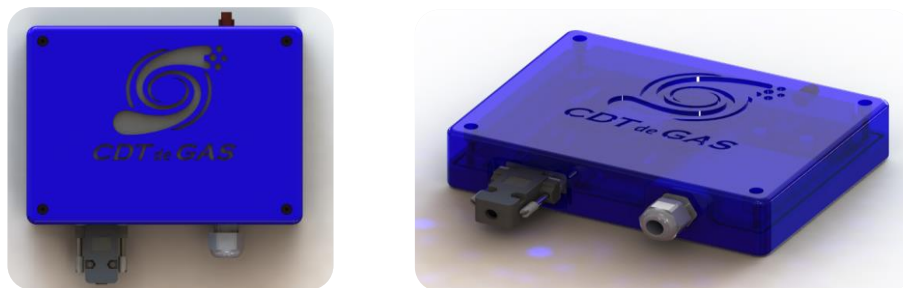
CAD Case ICU 1.0 diseño final de la primera versión. Fuente: Autor
